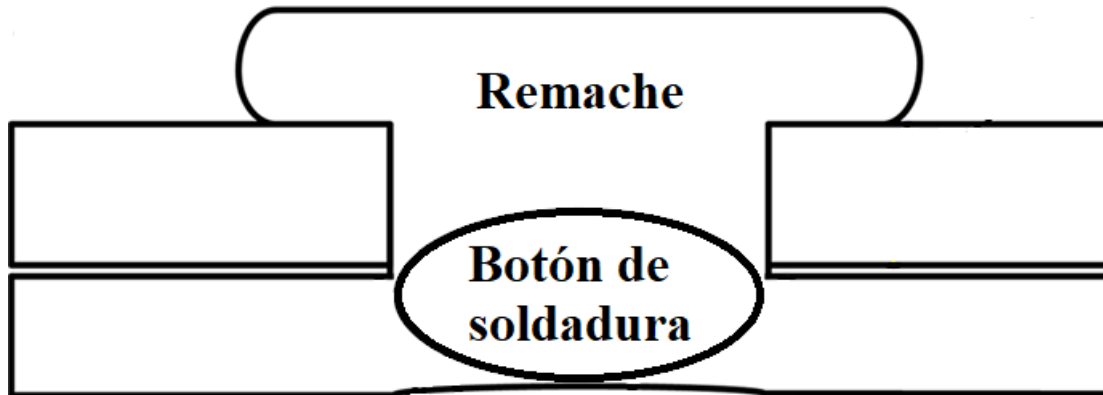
Esquema representativo de un botón de soldadura por REW [6].
